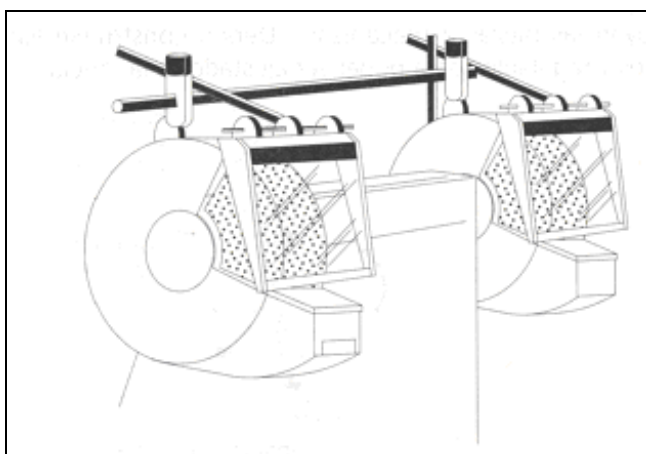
Pantalla montada sobre soporte adaptable a cualquier esmeriladora
